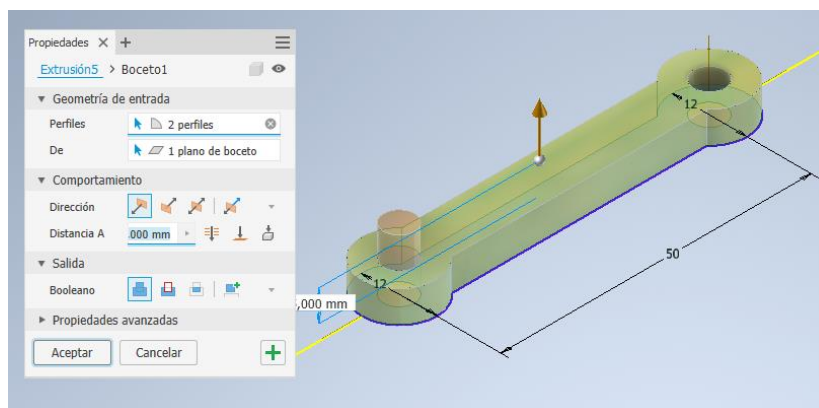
23. Extrusión del cuerpo principal del balancín superior
